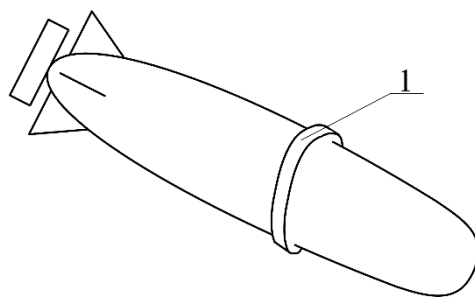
Установка катушки приемной части БСПЭ соленоидного типа (1) снаружи на корпусе АНПА
